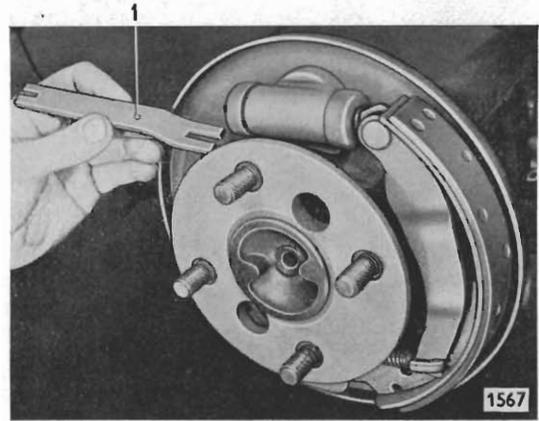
Druckstange in Bremsseilhebel einsetzen
